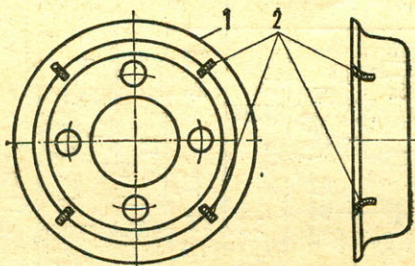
Размещение ребер на диске: 1 — диск; 2 — ребра, наплавляемые газосваркой.
